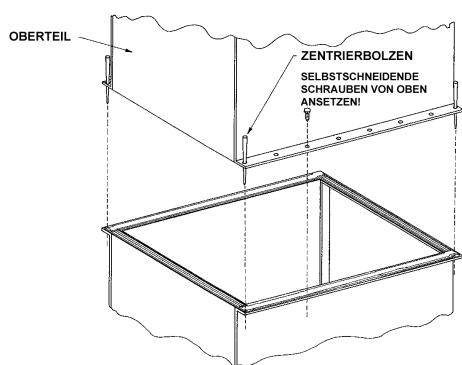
Verschrauben des Oberteils mit dem Unterteil
